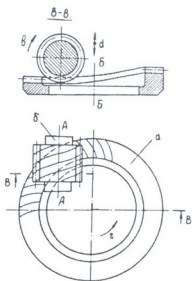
Схема нарезания спиридного зубчатого колеса
